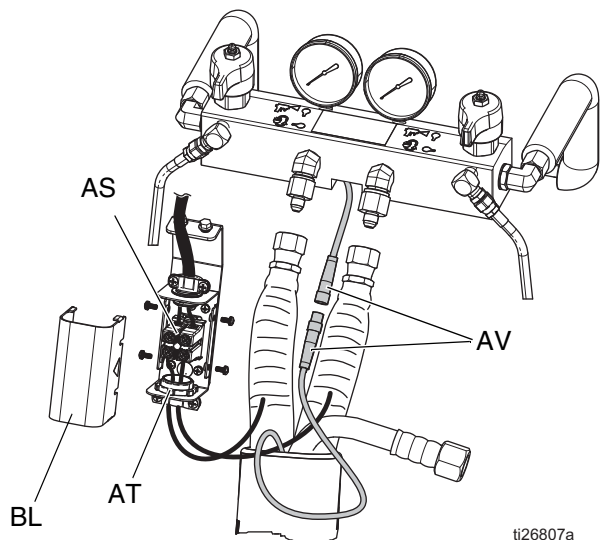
Connexion du flexible chauffant à la boîte à bornes
